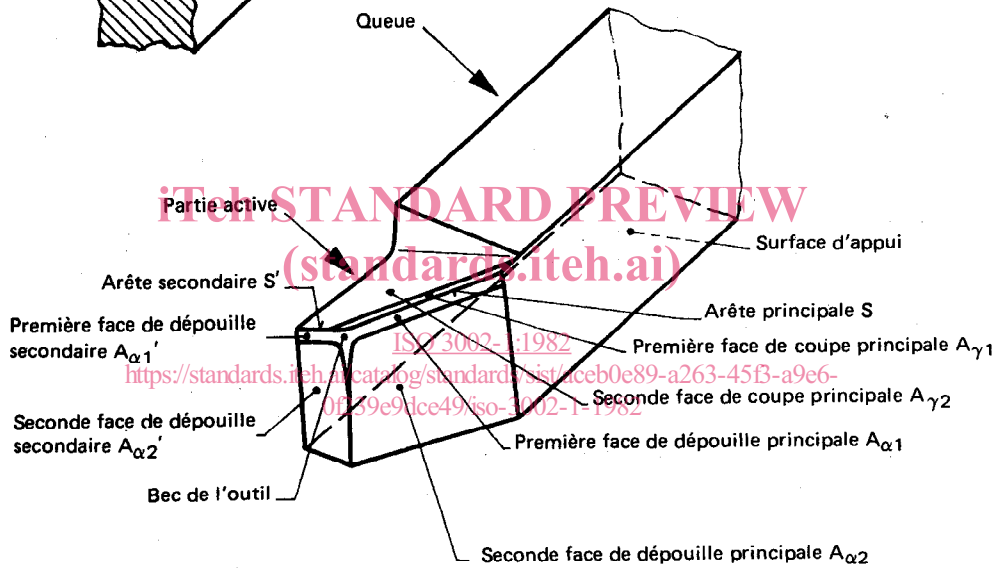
Arêtes et surfaces de la partie active d'un outil de tournage
